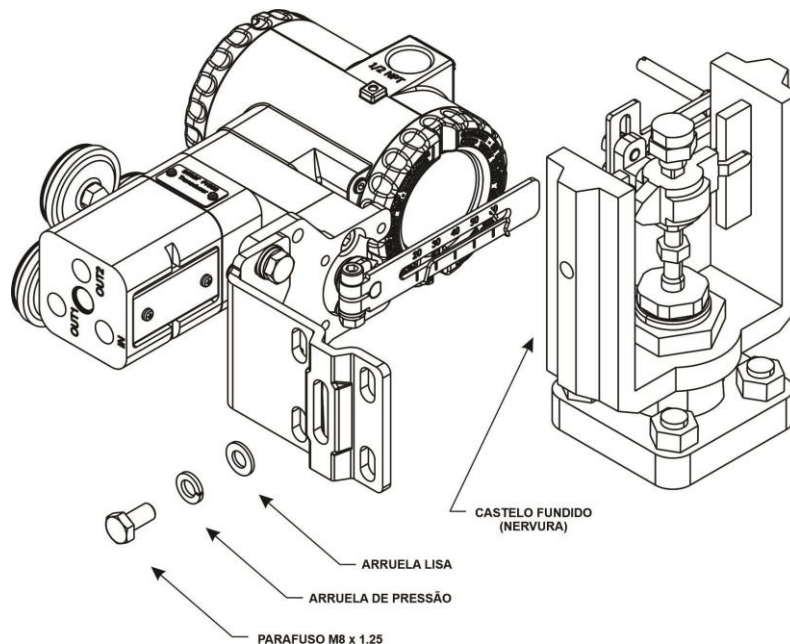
Fixação do suporte de montagem ao castelo fundido com superfície de nervura
